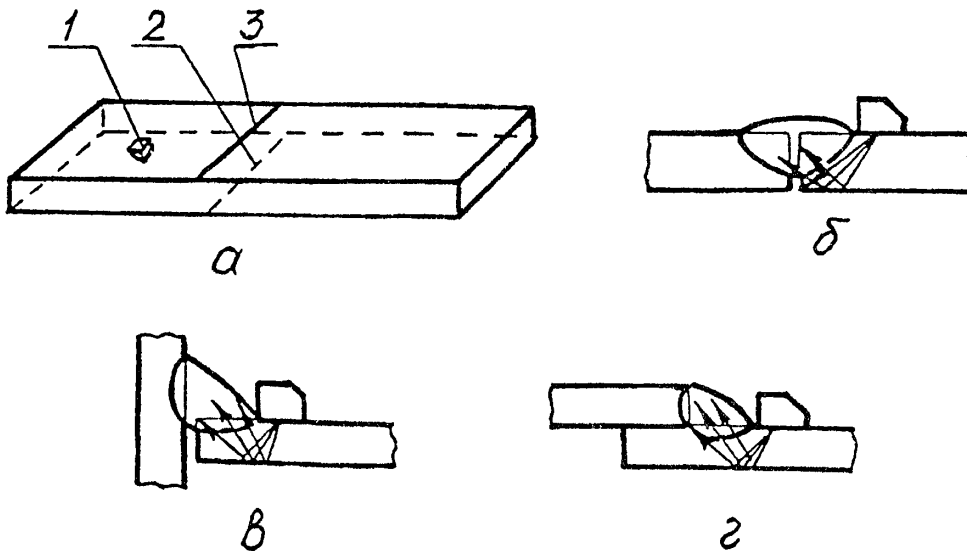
СОП (а) с рисками для проверки возможности озвучивания корня стыкового (б) и угловых (в, г) швов:
